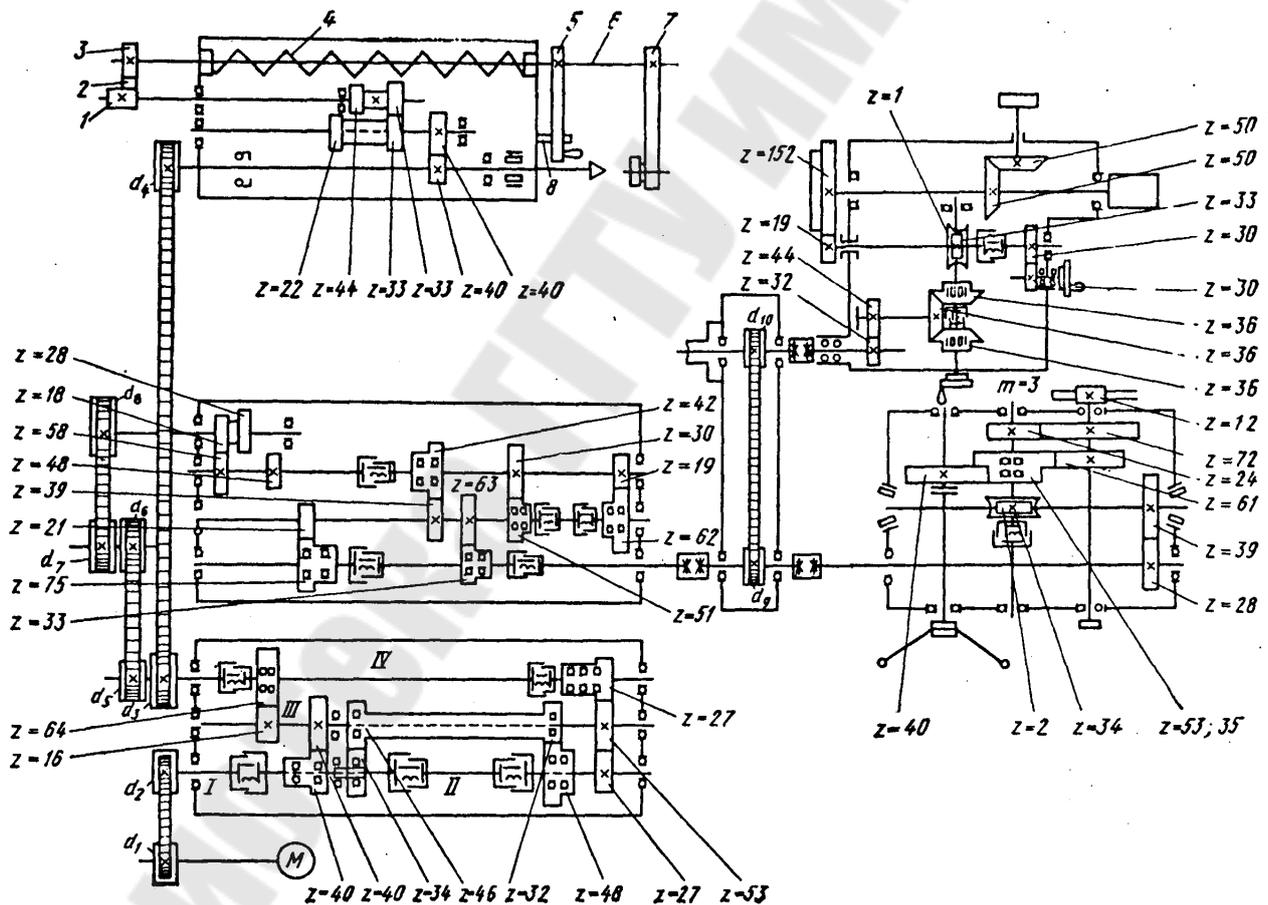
Кинематическая схема токарно-револьверного станка
